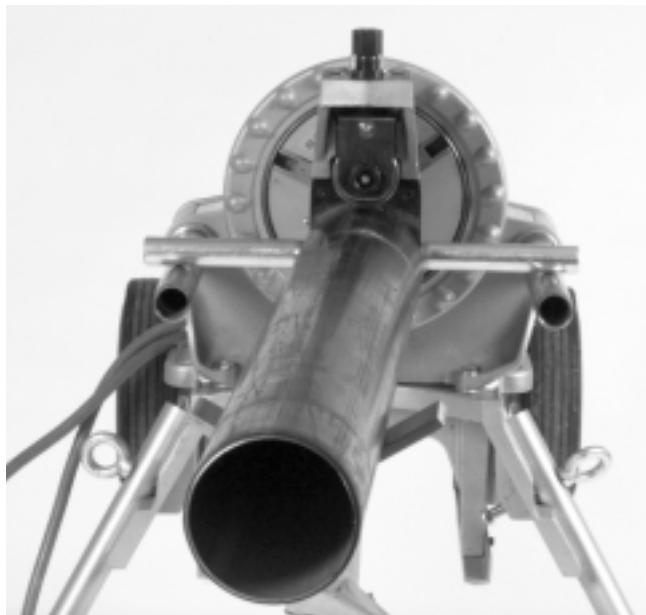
Primer plano del tubo contra la placa o cubierta
